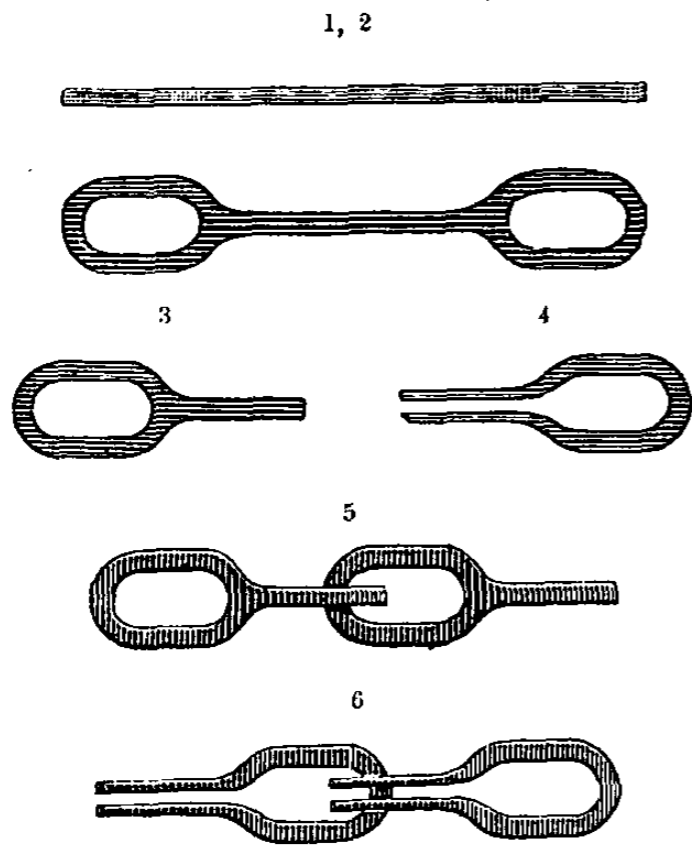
à 321. — Chaîne d'acier sans soudure, procédé David et Damoiseau.
